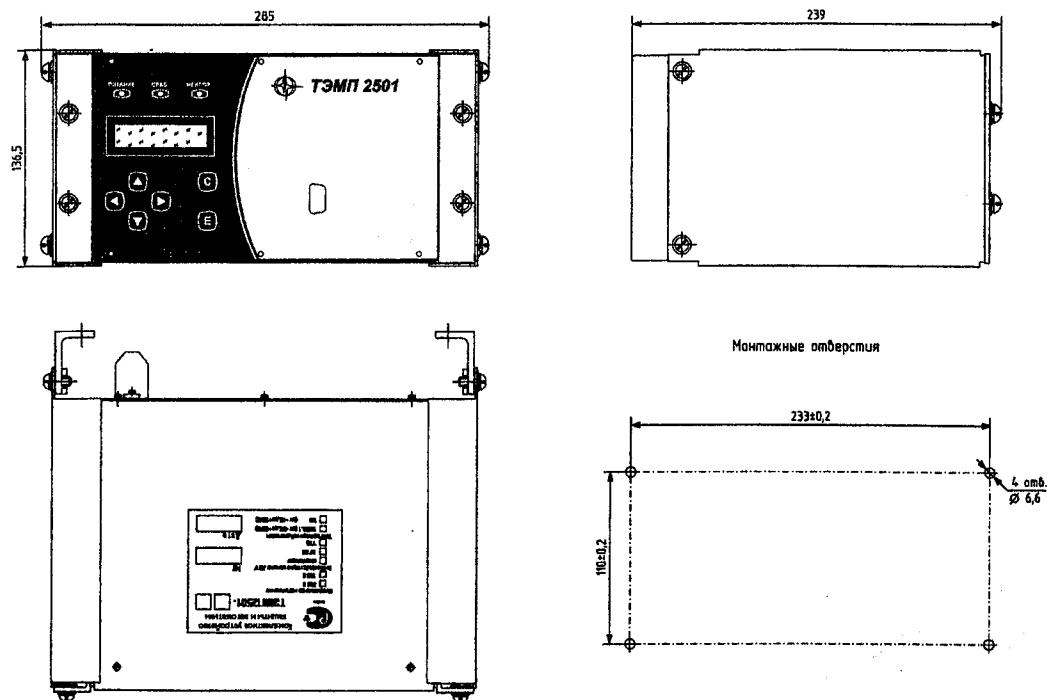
Габаритные и установочные размеры ТЭМП 2501-12/22/32/42
